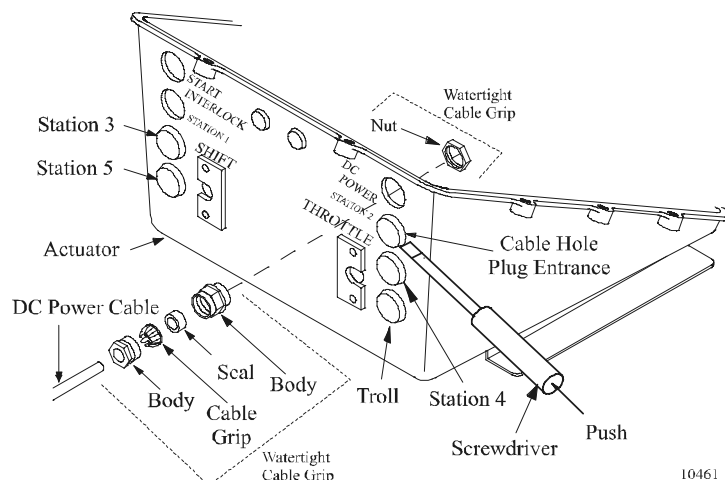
Entfernen der Stopfen und Anbringen der Kabeldurchführung
